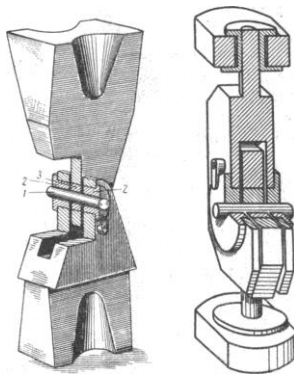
Приспособление к разрывной машине типа Р-5 и ИМ-4Р для испытания на срез: 1 – образец; 2 – захват нижний; 3 – захват верхний
